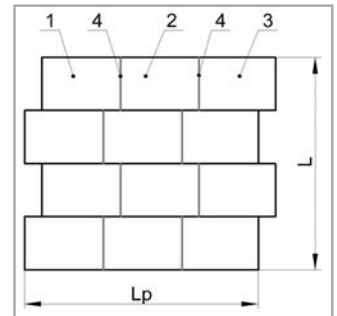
Схема условной развертки обечайки, свариваемой из царг: 1, 2 и 3 — листы составной развертки царги; 4 — продольный сварной шов царги; L<sub>p</sub> — длина развертки царги; L — длина обечайки
